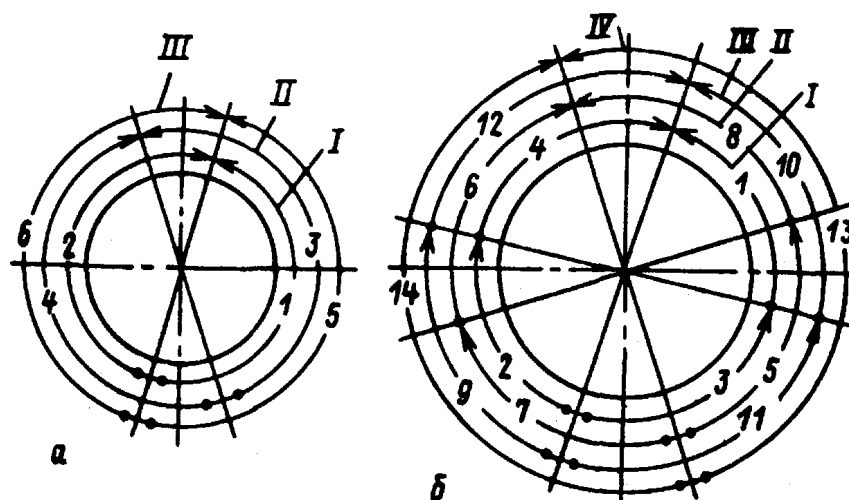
Порядок наложения слоев при сварке одним сварщиком вертикальных неповоротных стыков труб:
